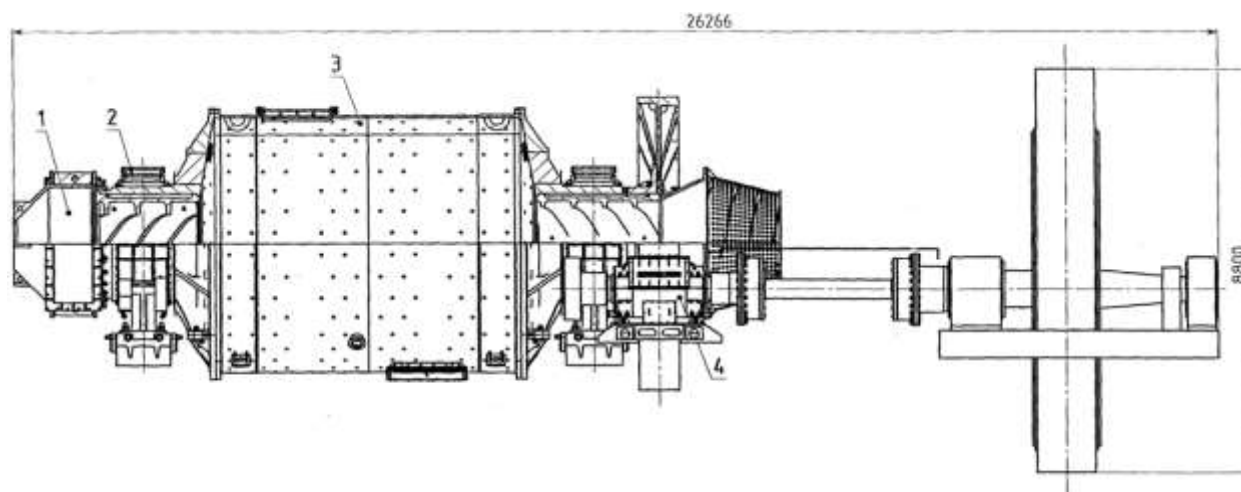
Конструкция МШЦУ-5500х6500А: 1 – питатель комбинированный, 2 – подшипник коренной, 3 – барабан, 4 – привод
